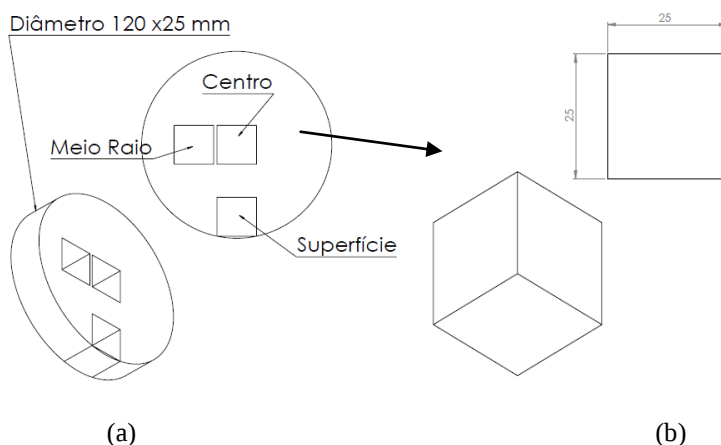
Desenho esquemático da preparação da amostra (a) – Identificação de posição e corte da barra (b) – Cubo fresado (O autor, 2017)
